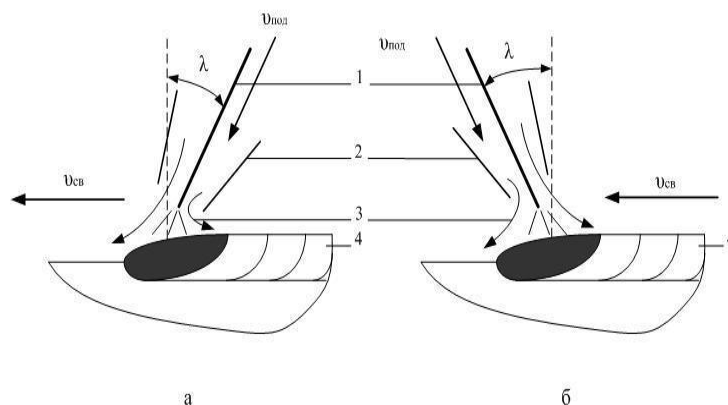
Способы полуавтоматической сварки в углекислом газе:
